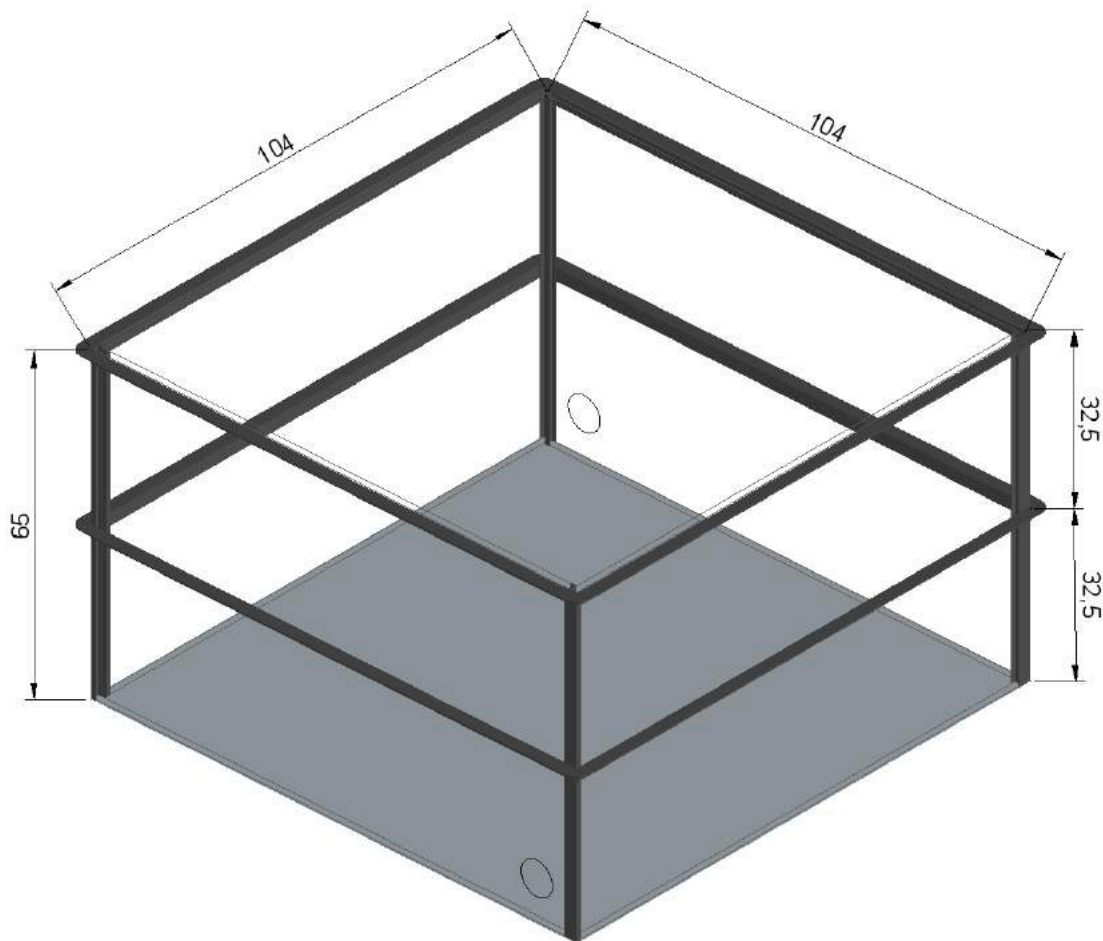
Representação 3D da caixa de vidro e estrutura metálica de suporte
